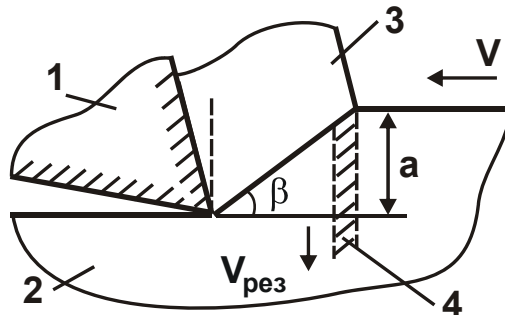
Расчетная схема процесса резания при точении: 1 – резец; 2 – обрабатываемый материал; 3 – образующаяся стружка; 4 – адиабатический стержень
